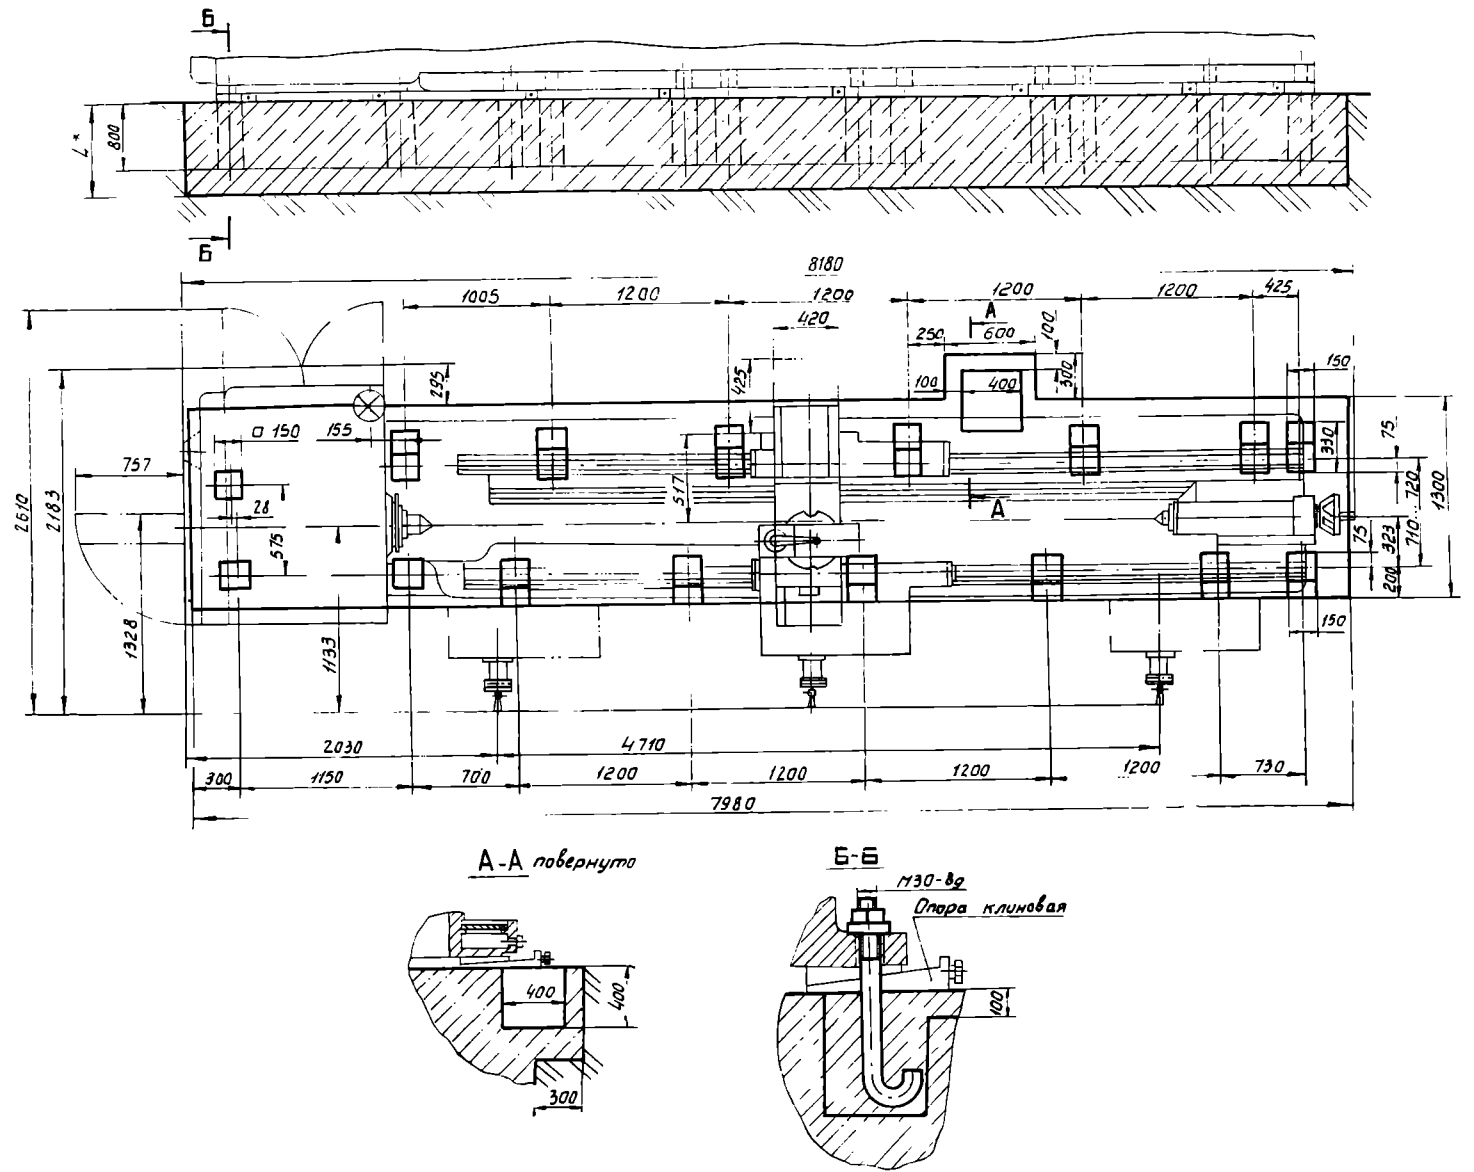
Монтажный (фундамент) и габаритный чертеж станка (PMЦ 5000 мм)
